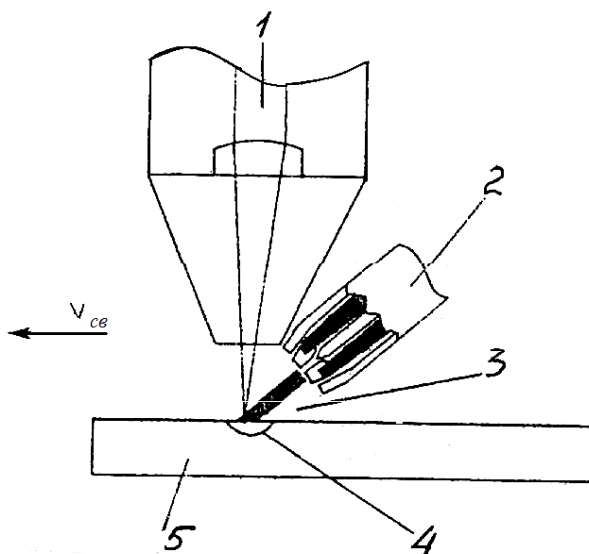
Схема комбинированного процесса лазерно-плазменной сварки: 1 – луч лазера; 2 – плазмотрон; 3 – плазменная дуга; 4 – сварочная ванна; 5 – свариваемое изделие
